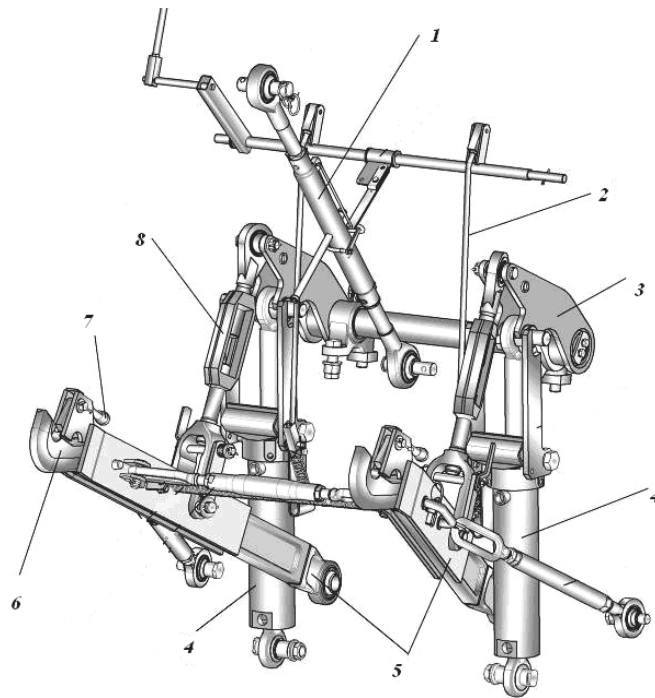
Механизм навески МЭС: 1 – тяга верхняя; 2 – тяга механизма фиксации; 3 – рычаг поворотный; 4 – гидроцилиндры; 5 – тяги нижние; 6 – захват; 7 – ручка фиксатора; 8 – раскос
